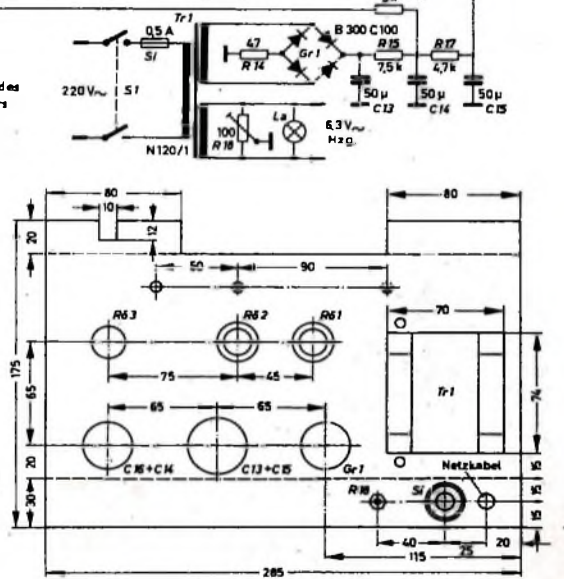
Anordnung der Einzelteile auf der Montageplatte
